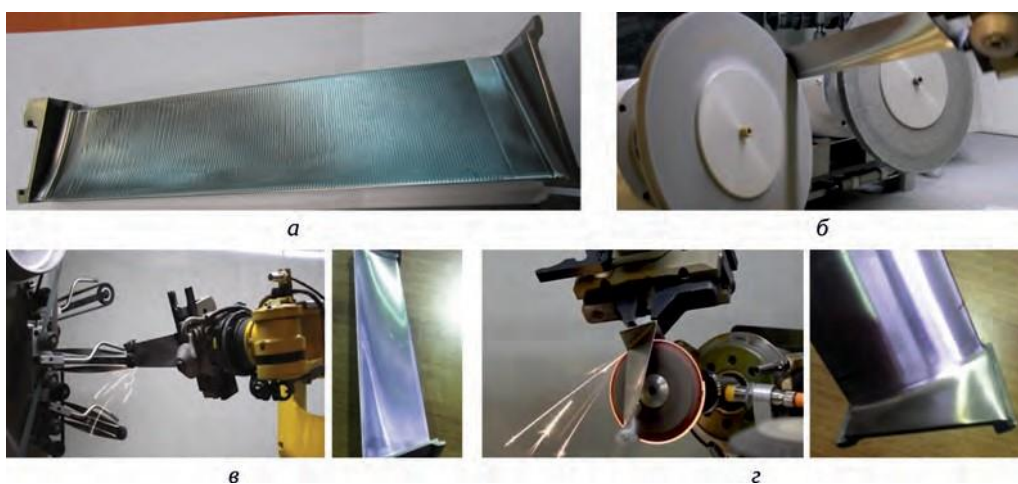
Переходы обработки поверхностей лопатки, применяемый инструмент и внешний вид шлифованной поверхности: а – перо лопатки после фрезерования; б – обработка кромок, снятие заусениц, формирование радиусов и фасок на кромке; в – неадаптивное ленточное шлифование спинки и корыта пера; г – неадаптивное шлифование абразивным кругом переходных частей
